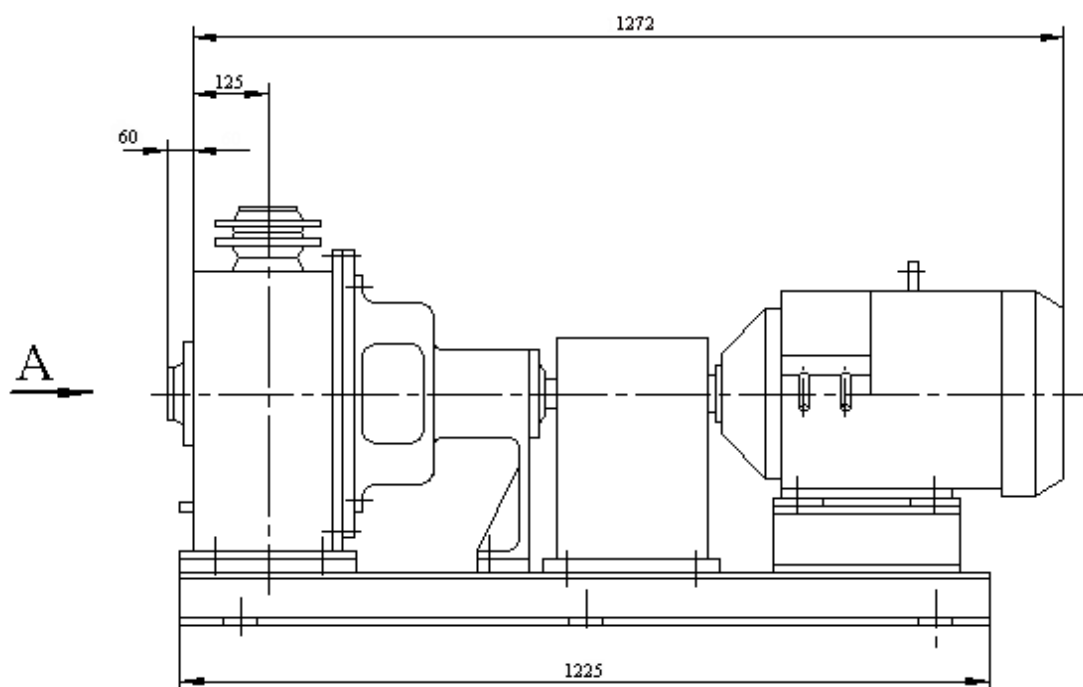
Габаритный чертеж насосного агрегата типа ЦНА 6,3/50
